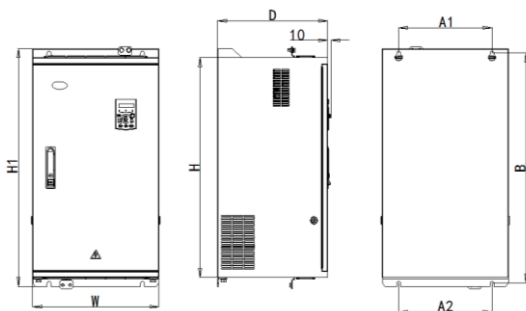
160kW~400kW外形尺寸及安装尺寸示意
